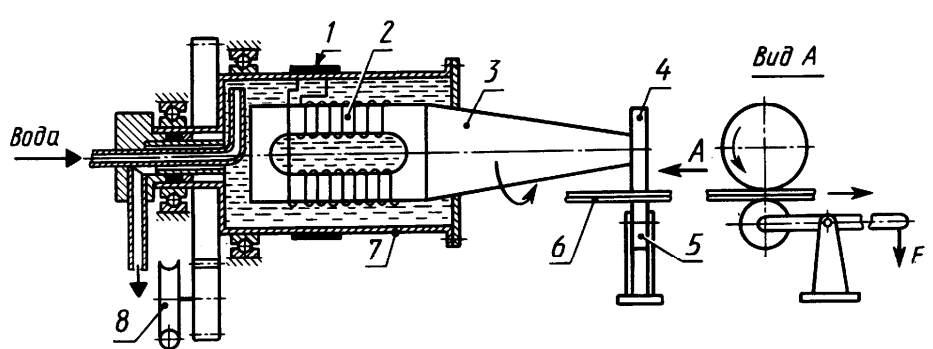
Принципиальная схема машины для ультразвуковой шовной сварки
